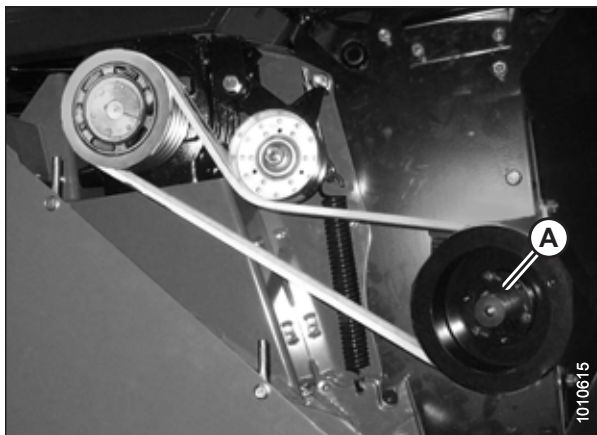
Courroie d'entraînement et poulies du côté gauche – Type tracté à disques rotatifs
